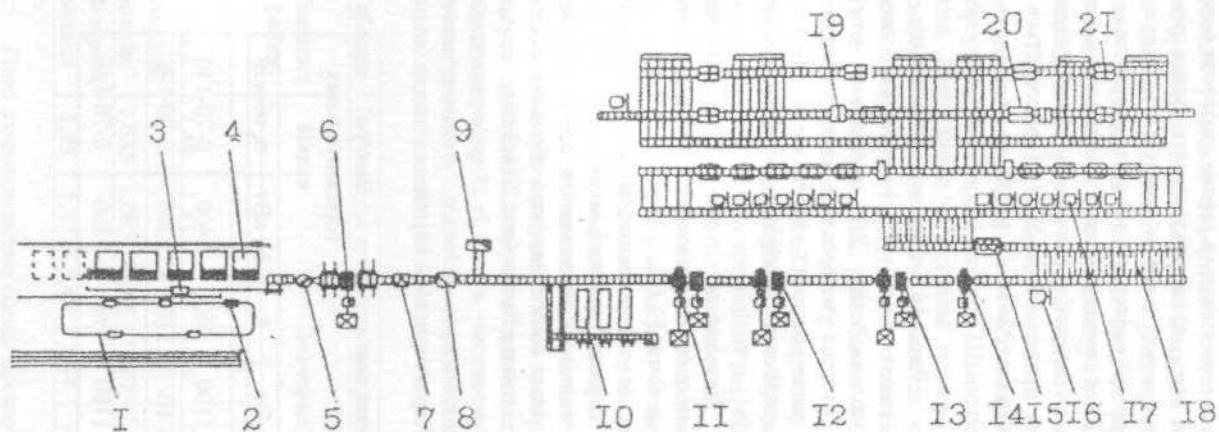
Універсальний балковий стан: 1 - кільцева зливкопередача; 2 - ваги; 3 - зливкоподача; 4 - нагрівальні колодязі; 5 - поворотний пристрій; 6 - обтискна кліть 1450; 7 - машина вогневої зачистки; 8 - ножиці; 9 - конвейер для прибирання обрізків; 10 - печі з шагаючим черенем; 11 - перша група клітей; 12 - друга група клітей; 13 - третя група клітей; 14 - чистова універсальна кліть; 15 - правильна машина; 16 - пила гарячого різання; 17 - пили холодного різання; 18 - стелажі; 19 - вертикальний правильний прес; 20 - горизонтальний правильний прес; 21 - пакетуючий пристрій
